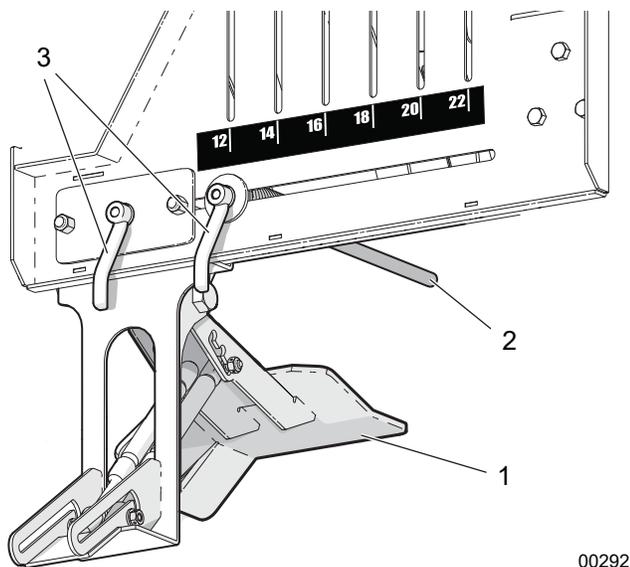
Déposeur de bûches et guide de butée des grumes
